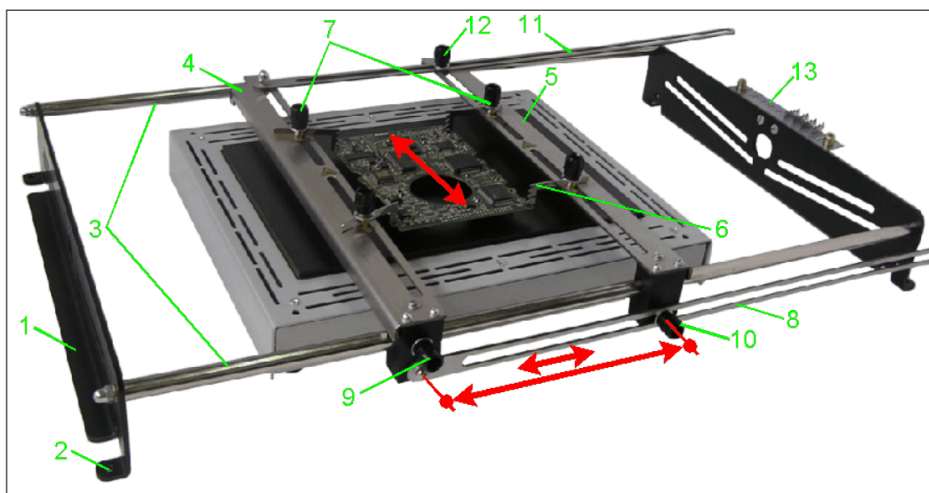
Внешний вид рамочного держателя печатных плат
